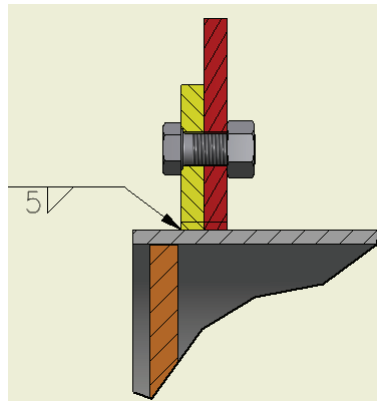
Lado soldado del soporte de la cuchilla trilladora
